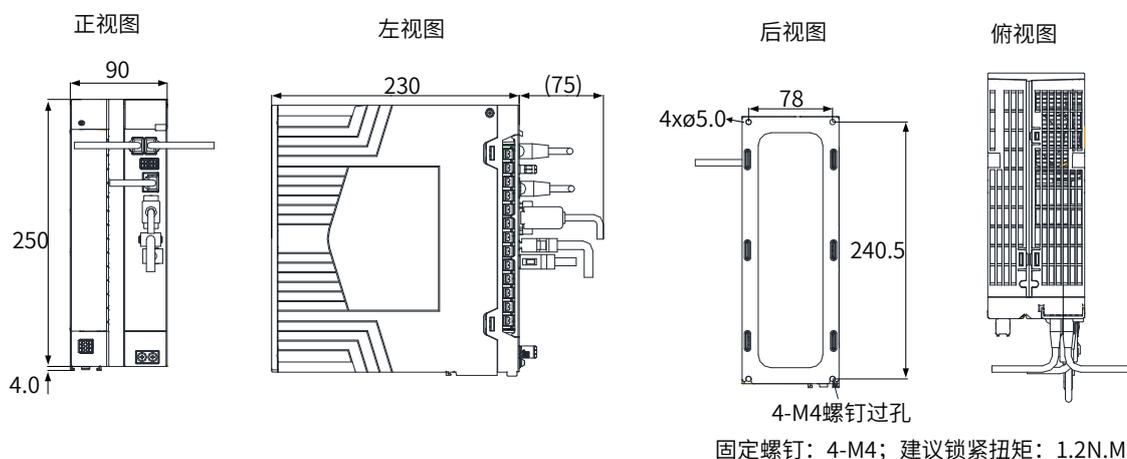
SIZE E 外形尺寸图 (单位: mm)
